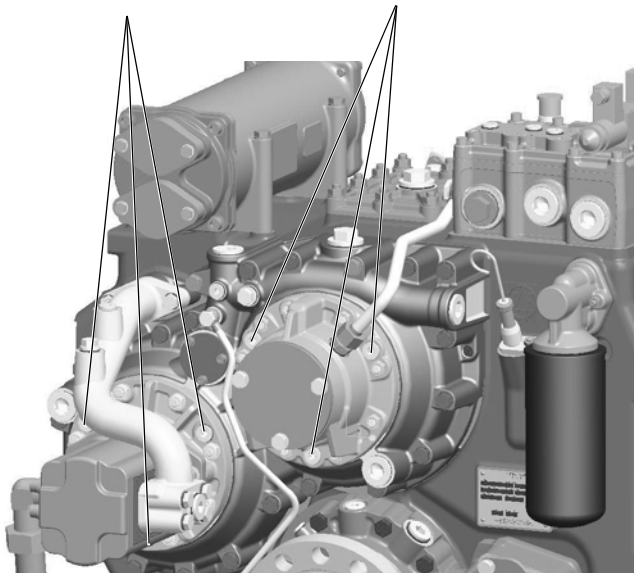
Lage der Spannschrauben für Gleich- und Gegenlauf (ZF 3150 A, Beispiel)
